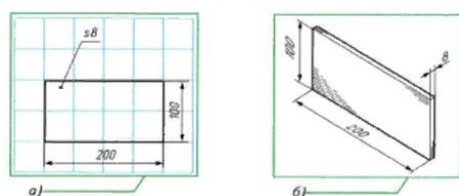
Эскиз (а), чертёжи (б) деталей швейного изделия
